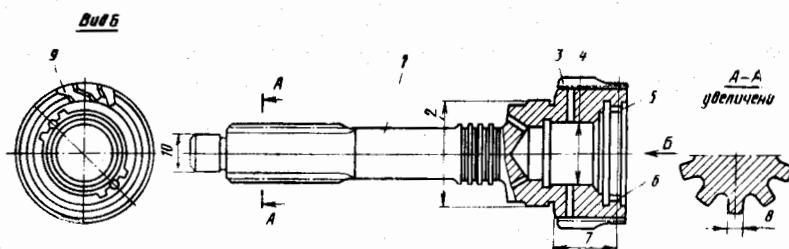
Основные дефекты ведущего вала коробки передач автомобиля ЗИЛ-431410
